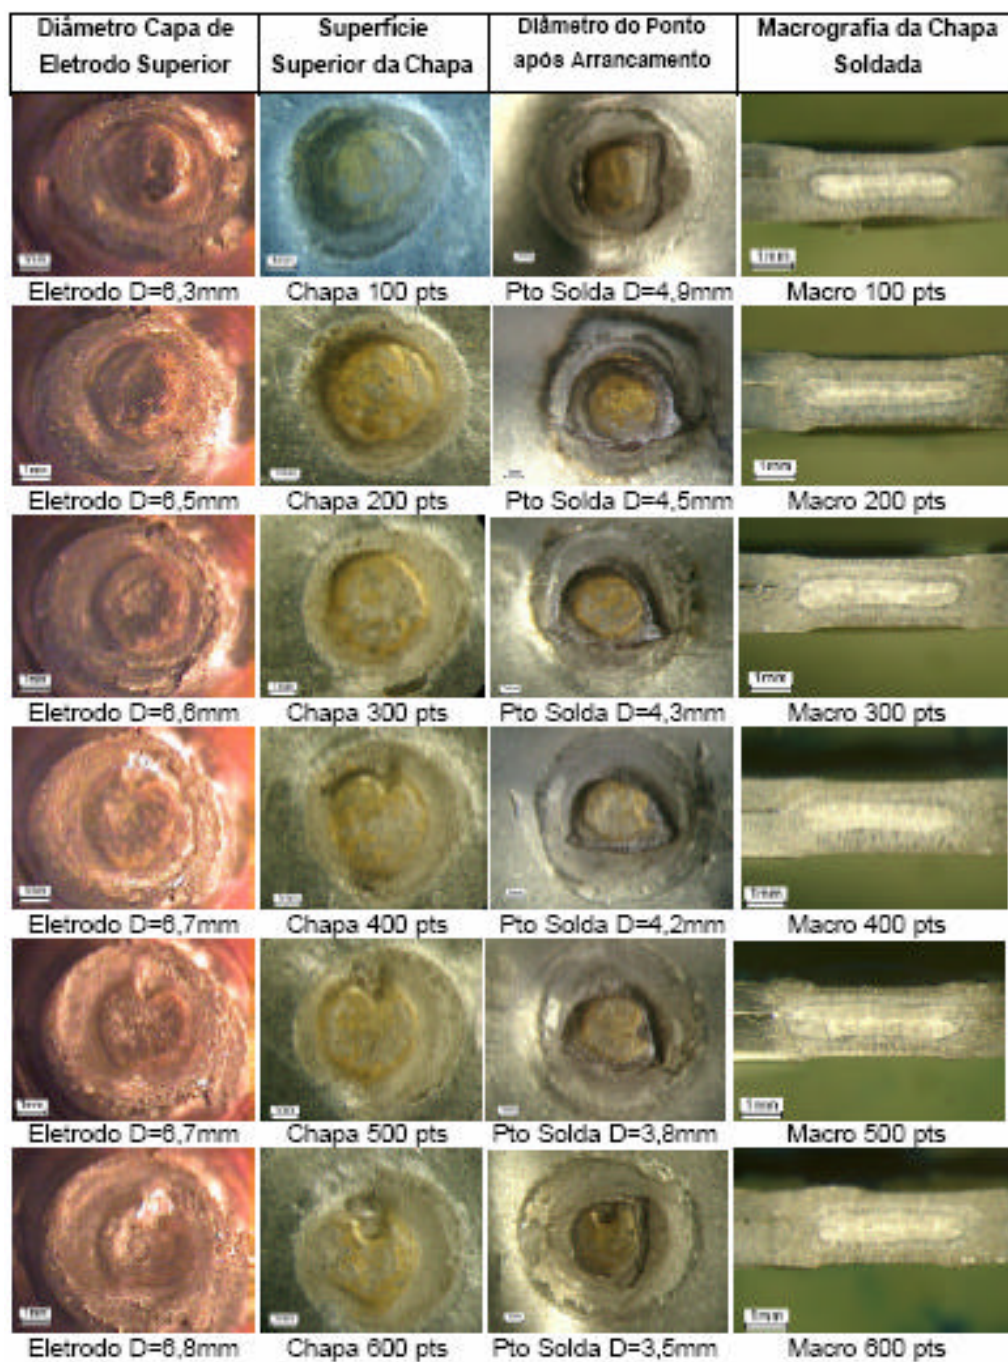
Pontos soldados com a capa de eletrodo B.
